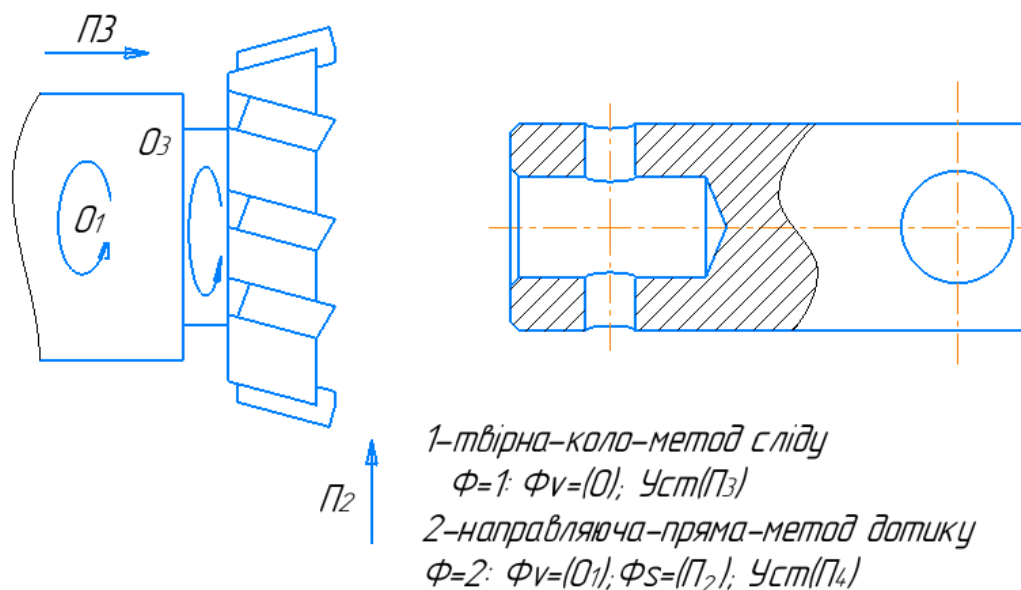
Обробка торцевою фрезою (основні формоутворюючі рухи)
